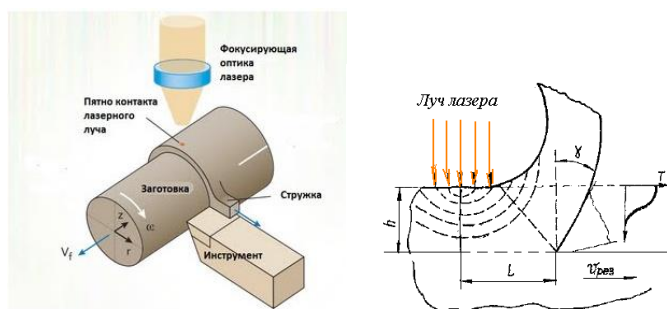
Схема резания металла в условиях его предварительного нагрева лазерным излучением
